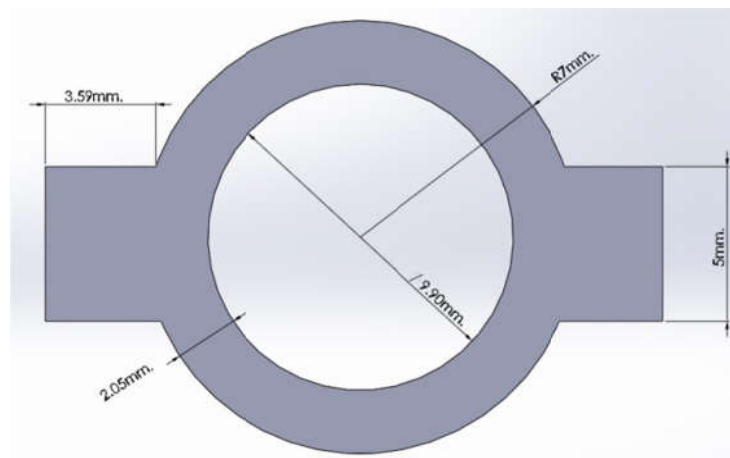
Vista frontal del conector para el carrete diseñado en el software Solidworks y contruido por un aimpresora 3D.
